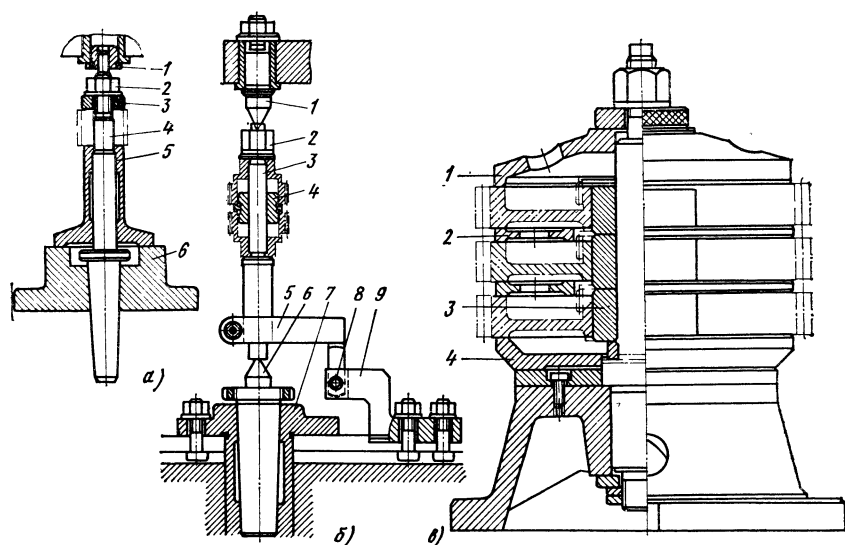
Переналаживаемые приспособления для обработки зубьев зубчатых колес на зубофрезерных станках
